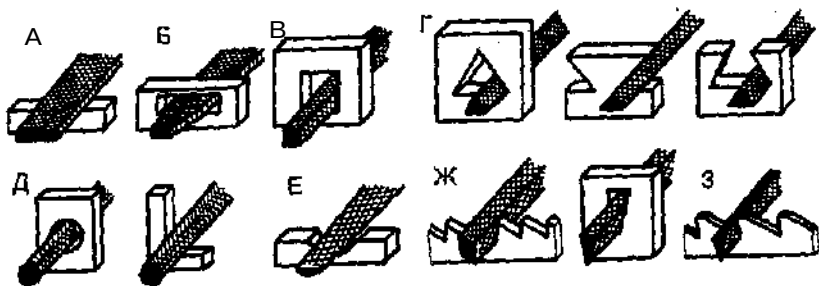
Напильники по форме сечения: А — плоские; Б — плоские остроносые; В — квадратные; Г — трехгранные; Д — круглые; Е — полукруглые; Ж — ромбические; З — ножовочные
